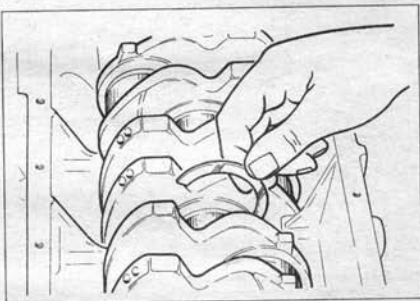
Установка упорных полуколец коленчатого вала в гнезда среднего коренного подшипника
